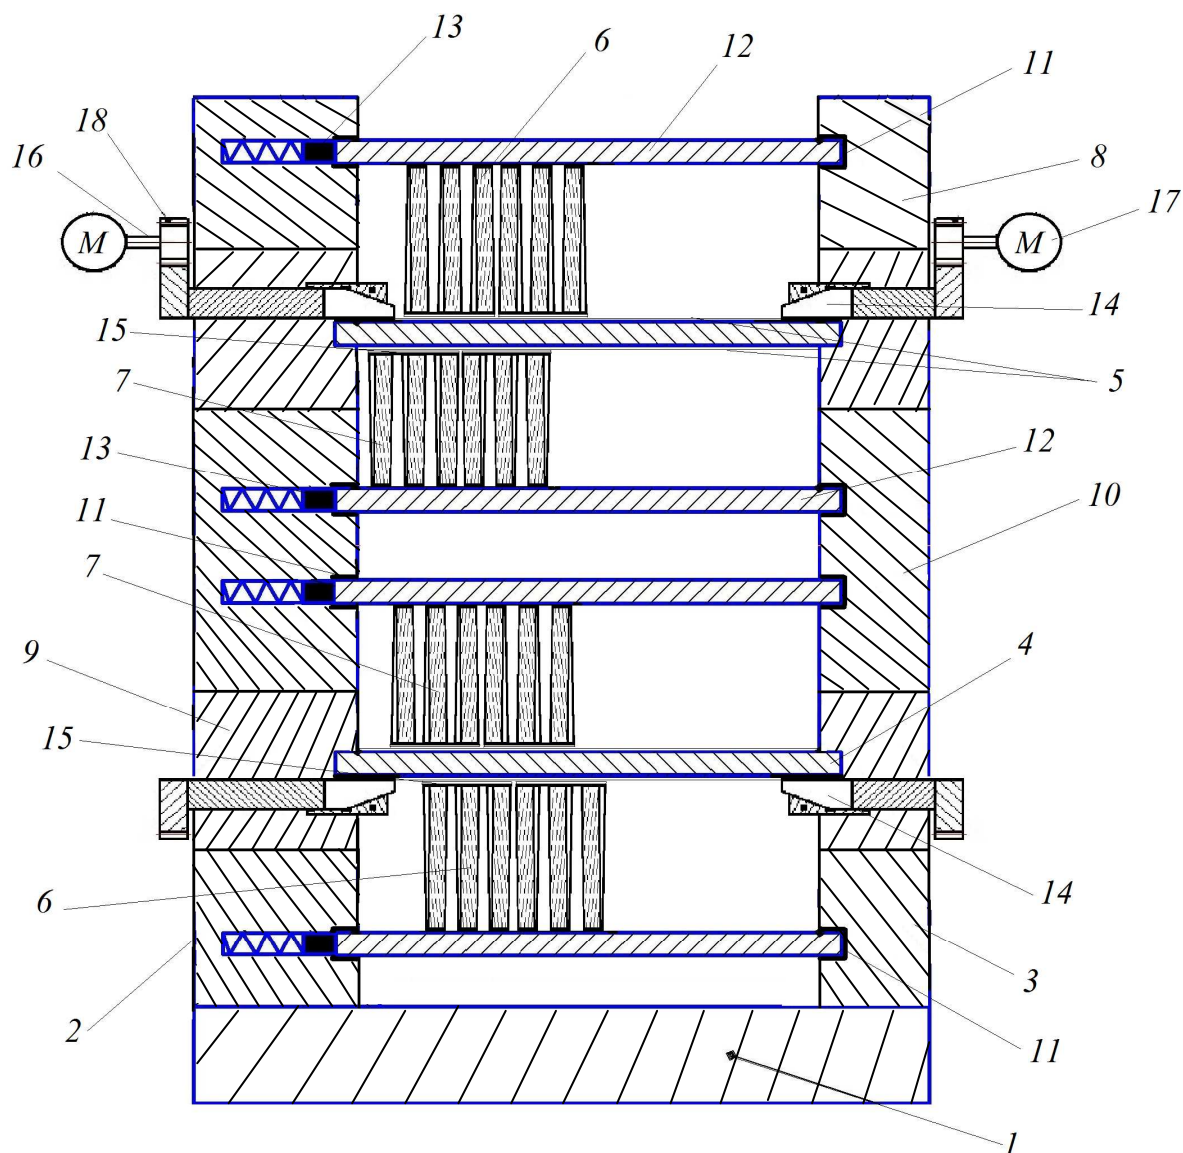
Устройство для хонингования одновременно наружных и внутренних поверхностей длинномерных цилиндров
